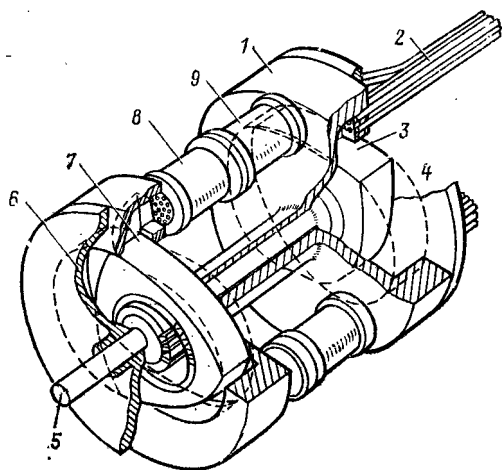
Схема Цвауэра — Ванкеля роторного двигателя Стирлинга.
